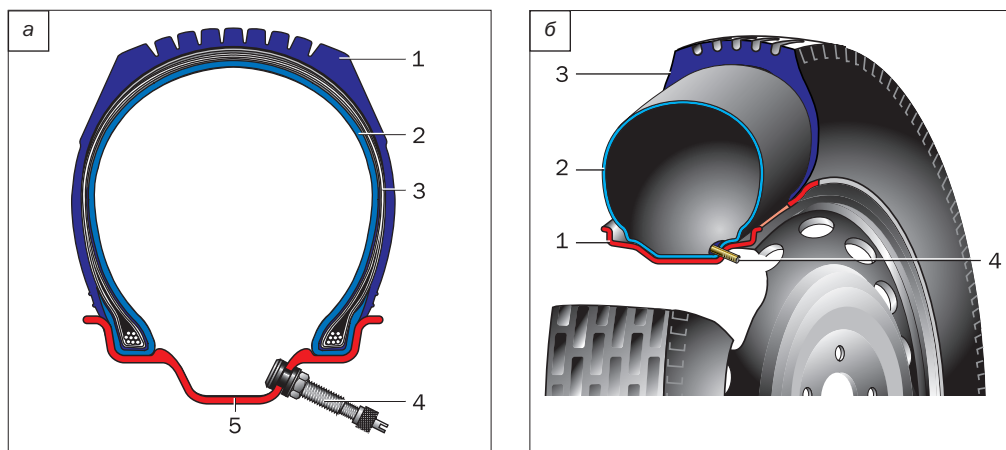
Конструкция колеса (а) с бескамерной шиной: 1 — протектор; 2 — герметизирующий воздухонепроницаемый резиновый слой; 3 — каркас; 4 — вентиль колеса; 5 — обод; (б) колеса с камерной шиной: 1 — обод колеса; 2 — камера; 3 — шина (покрышка); 4 — вентиль
